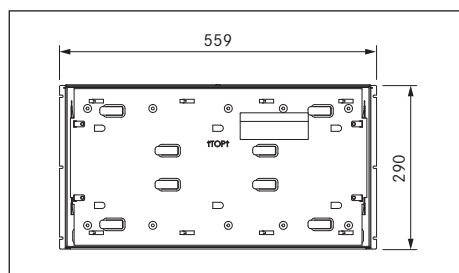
Dimensões do aparelho MS290, vista frontal
